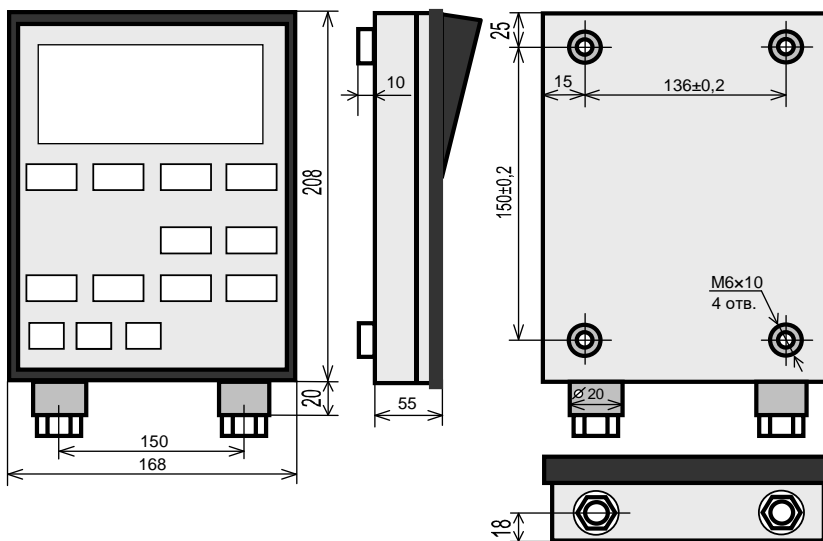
Габаритные и присоединительные размеры БОИ
